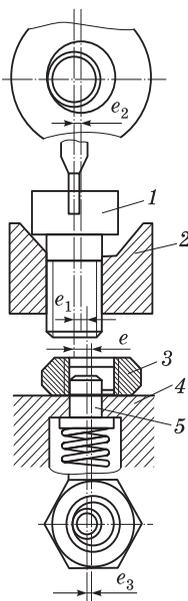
Несовпадение осей при сборке двух резьбовых деталей
